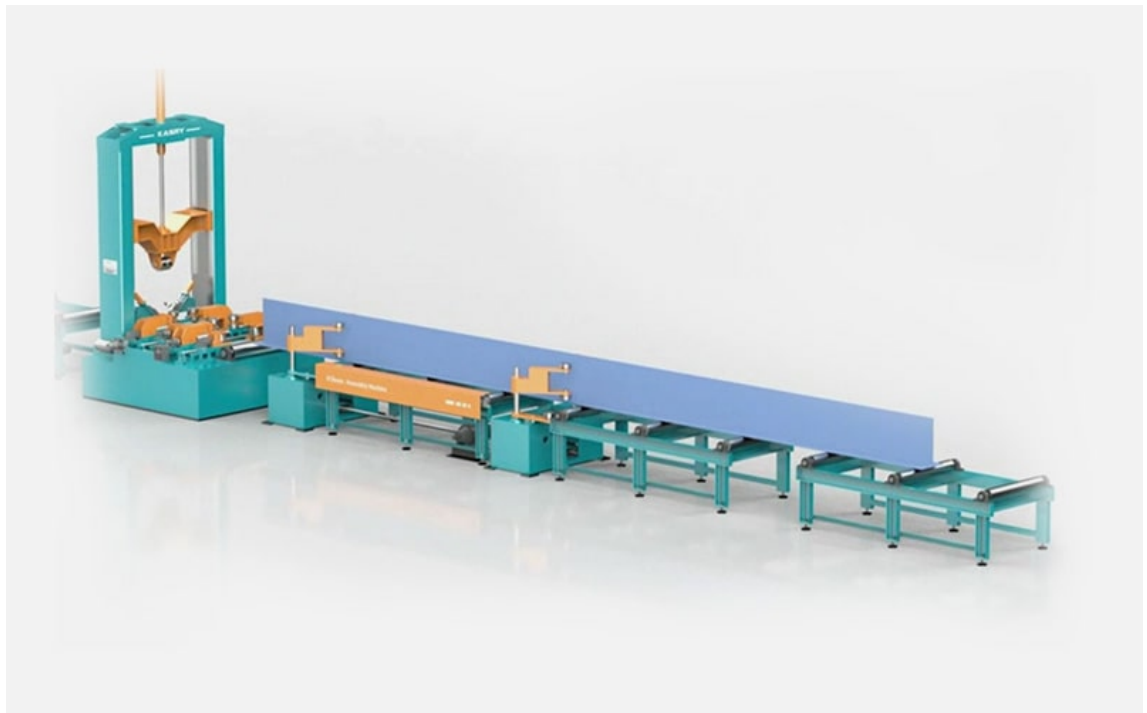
Верстат для складання та зварювання двотаврової балки KR-ZL-0818
